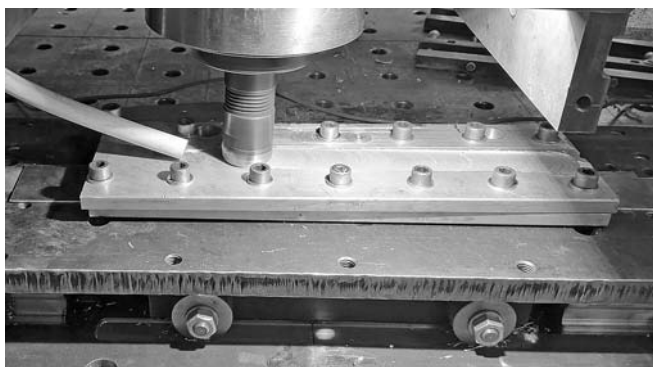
Сварка внахлест пластин из сплава АД31
